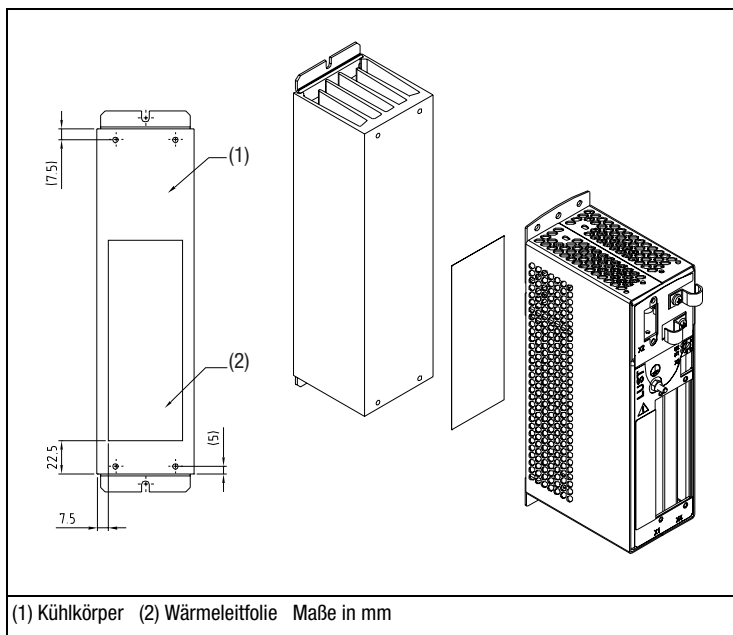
Montageplan Kühlkörper HS12.005/ Gerät ED12.005,Cx.x
